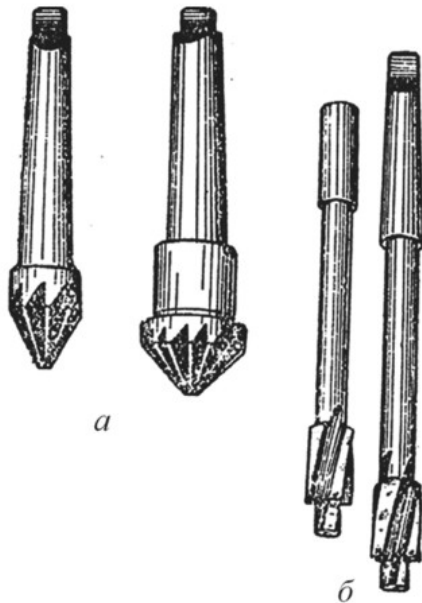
Зенковки: а) - конические, б) - цилиндрические.
